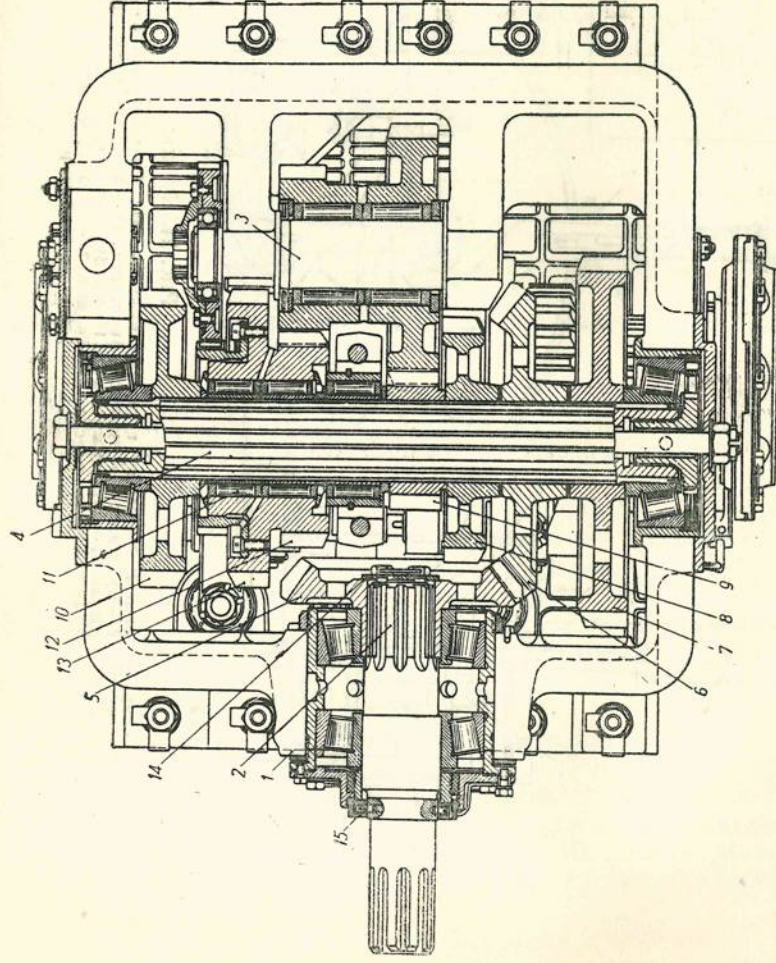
Разрез коробки перемены передач по осям ведущего, промежуточного и главного валов.
